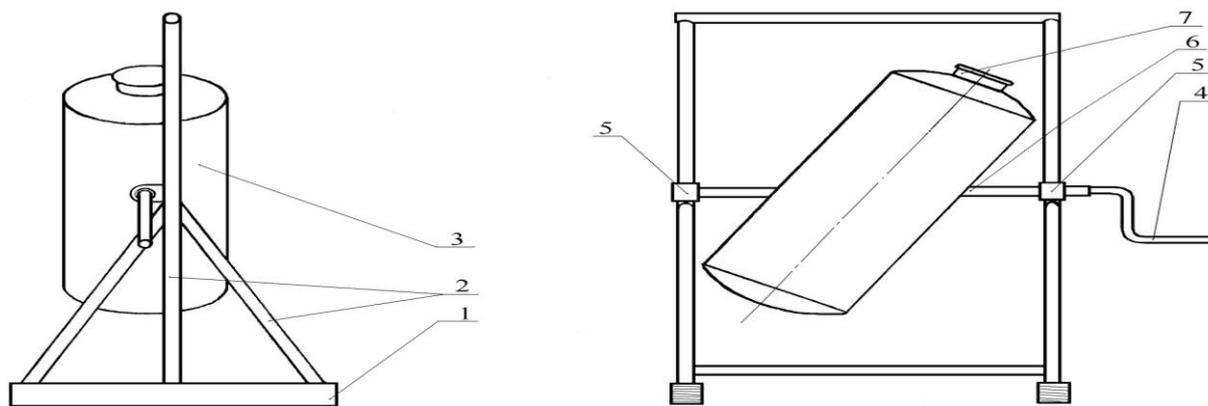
Протравливатель семян: 1 – основание; 2 – стойки; 3 – резервуар 20 дм³; 4 – рукоятка; 5 – подшипники; 6 – вал; 7 – горловина
